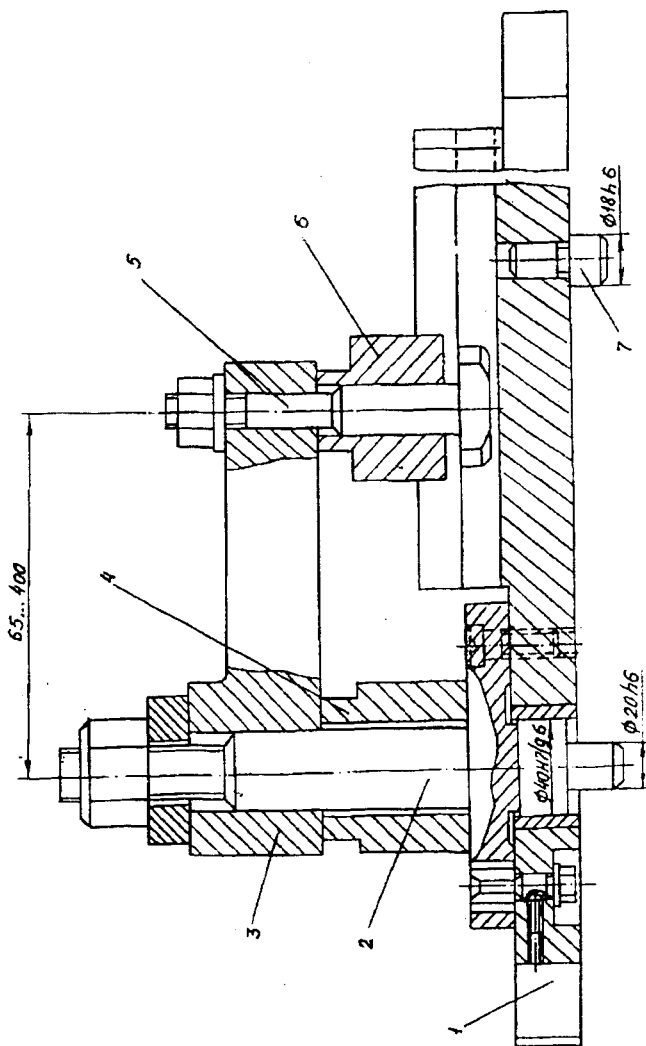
Передвижное приспособление для обработки контуров заготовок
